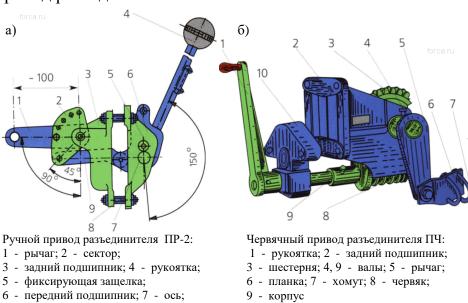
Общий вид ручного привода разъединителя ПР-2 (a) и червячного привода разъединителя ПЧ (б).
